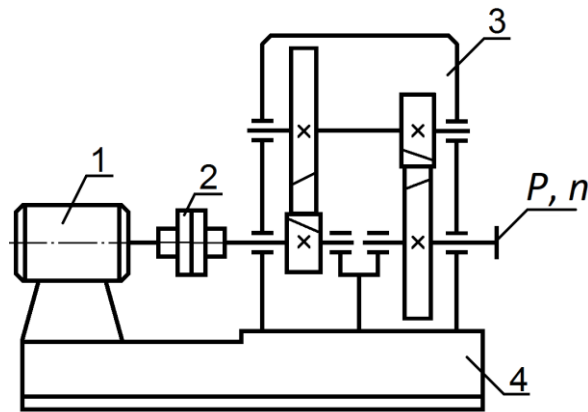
Привод винтового конвейера: 1 – электродвигатель; 2 – упругая муфта; 3 – двухступенчатый вертикальный соосный редуктор; 4 – литая плита
